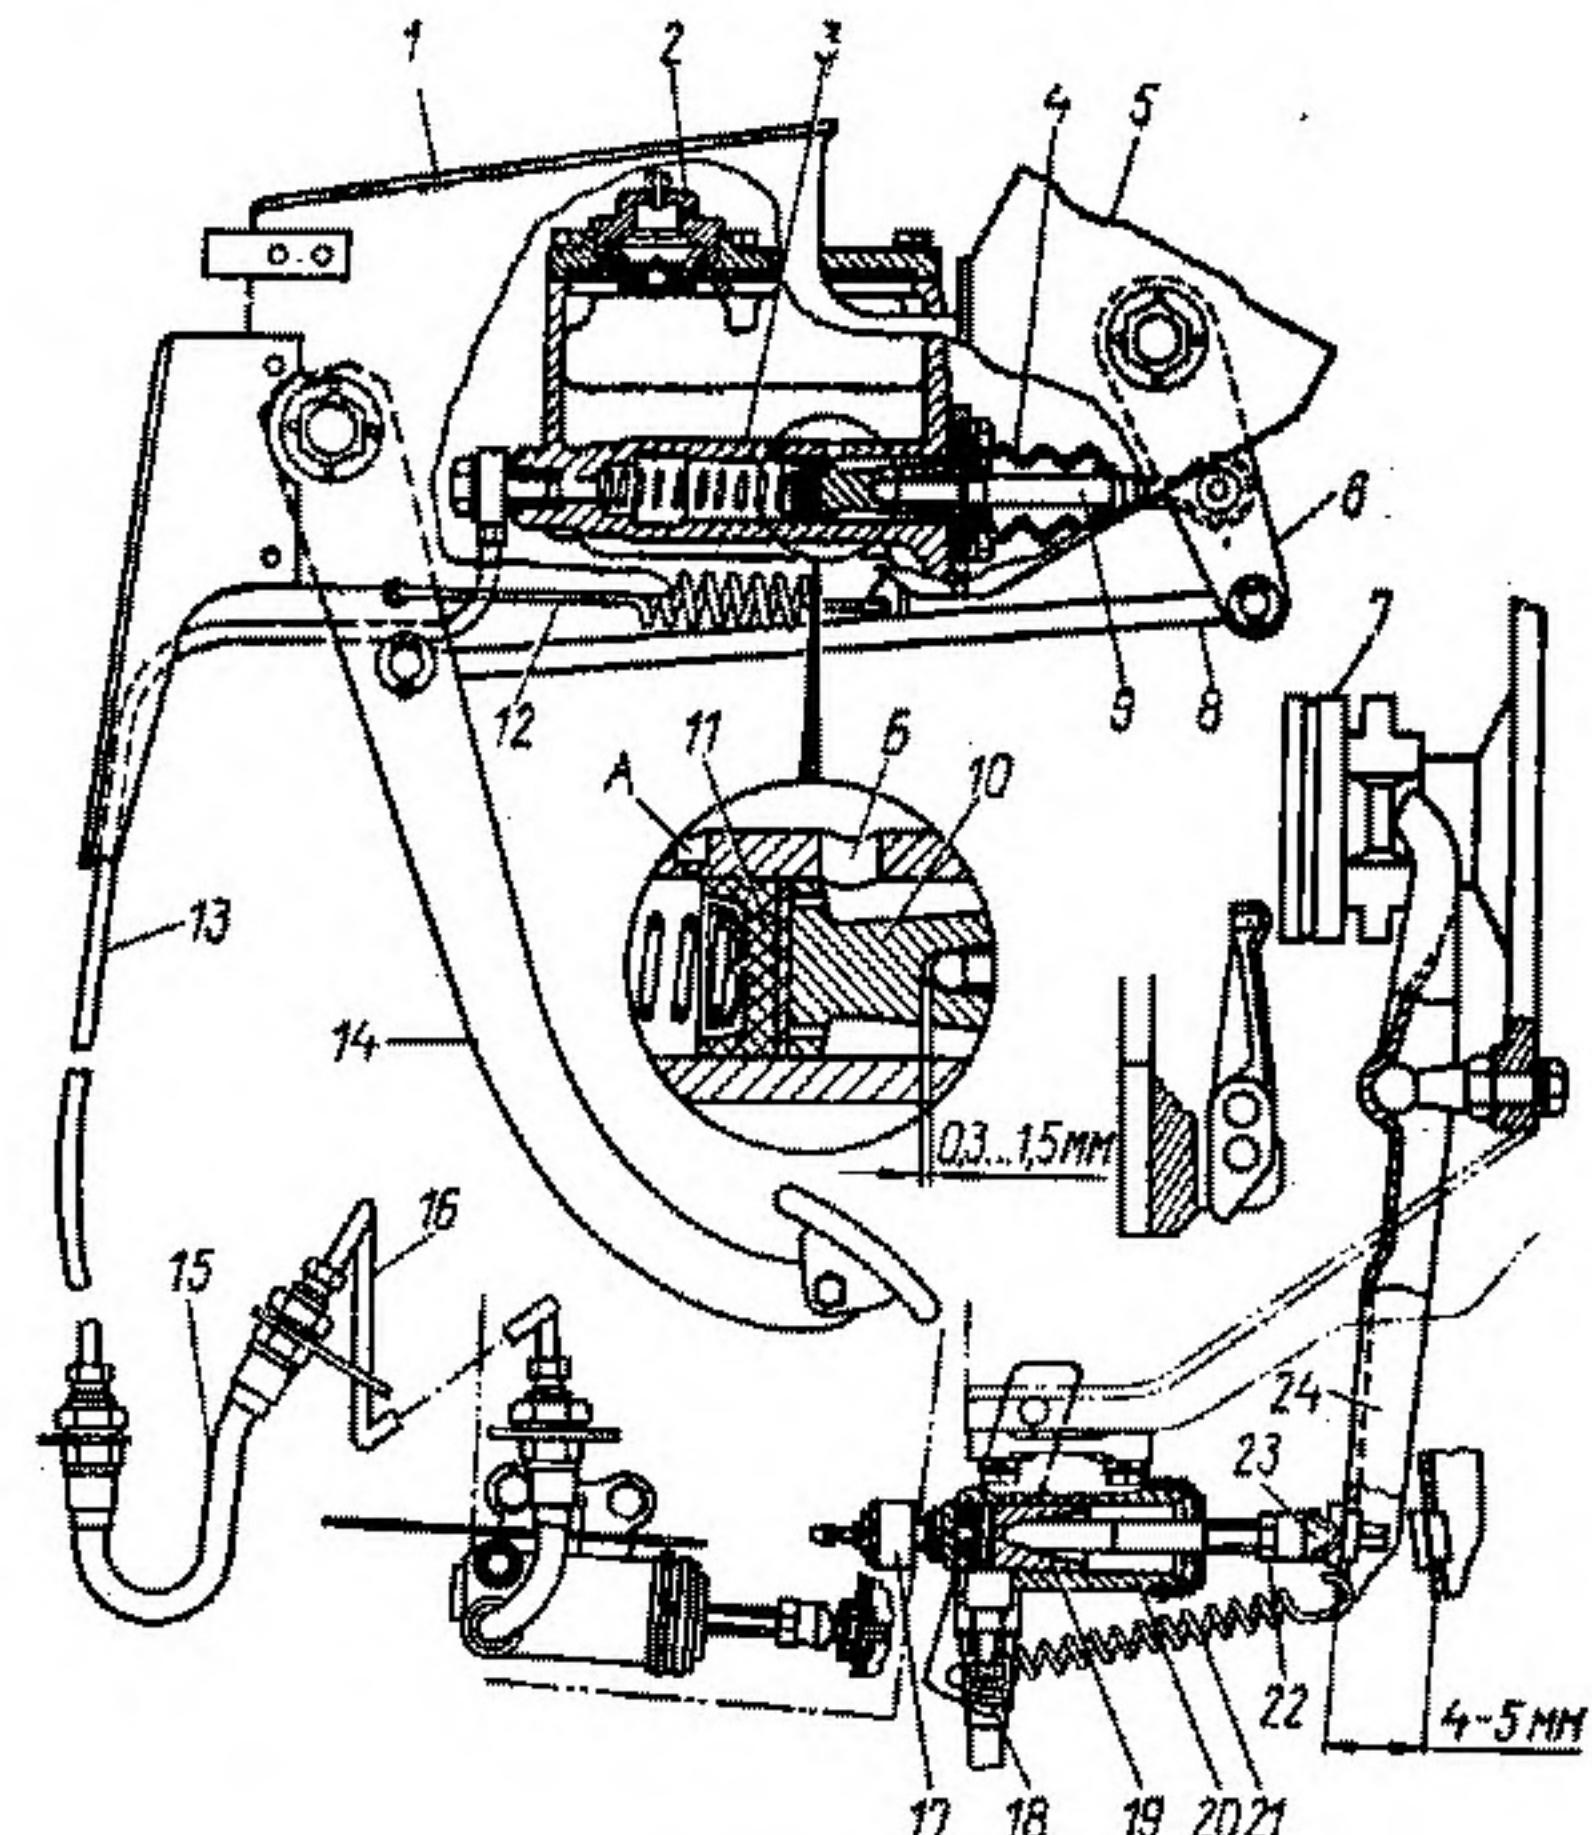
Привод сцепления автомобиля ГАЗ-66-11:
